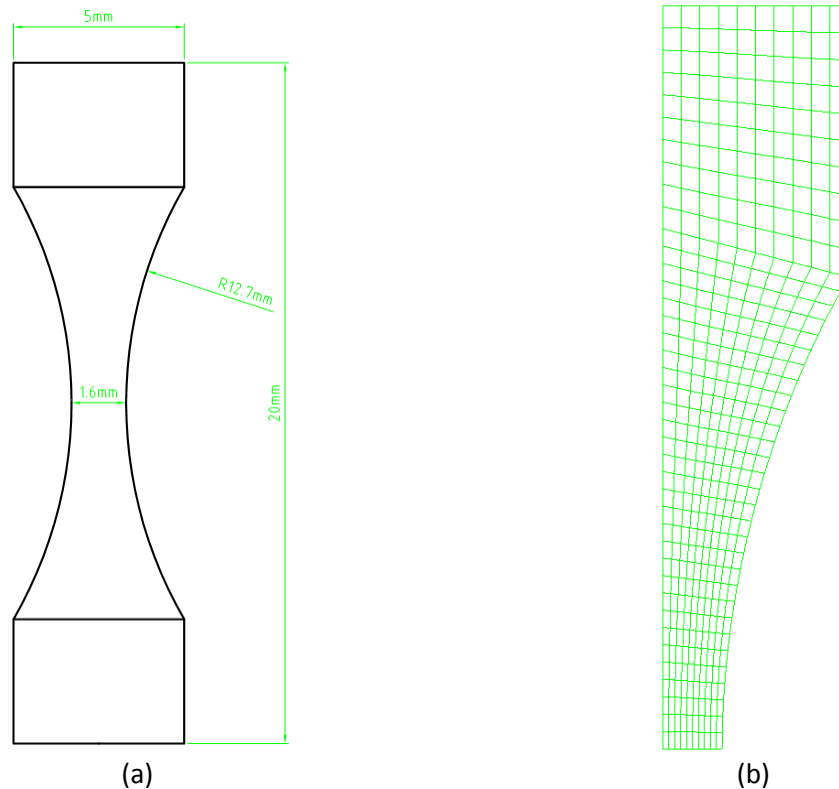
Provete para ensaio de tracção em estado plano de deformação (Bai, 2008). a) Geometria do provete. b) Malha de elementos finitos constituída por 400 elementos.
